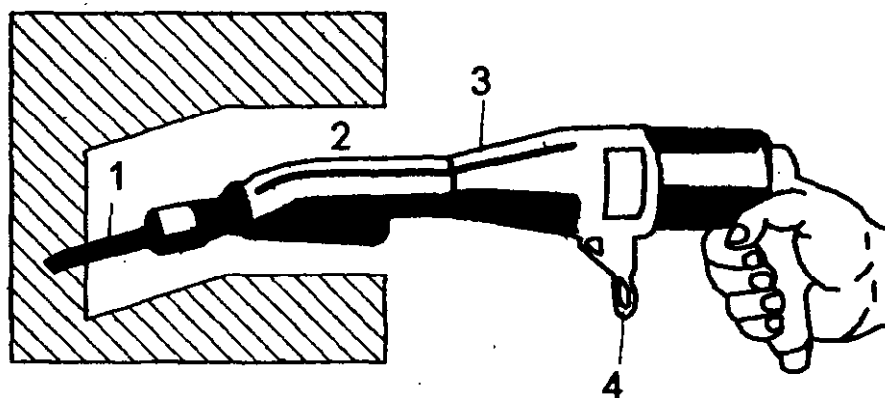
Пневматическая сверлильная машина РС-8 с угловой насадкой
